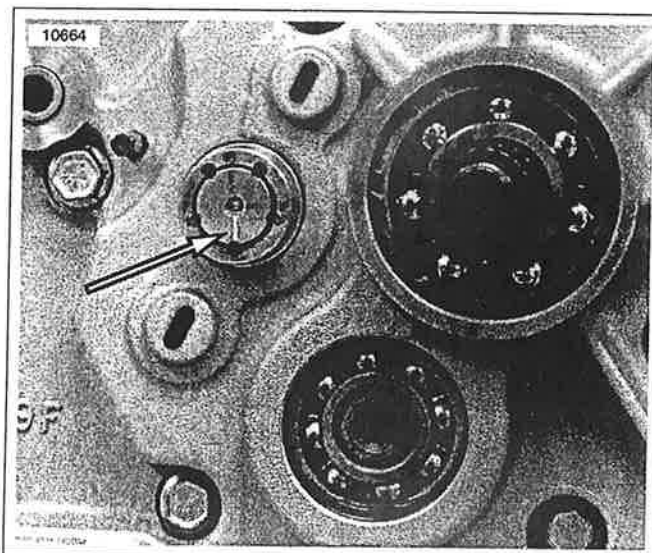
Línea marcada en el tambor de cambios en la posición de las 6 horas del reloj (transmisión en el engranaje de 4ª)
